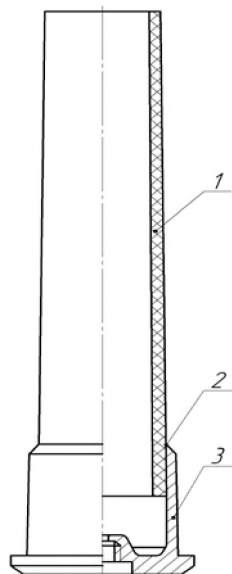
Гильза со сгорающим корпусом: 1 – корпус; 2 – мastic; 3 – поддон
